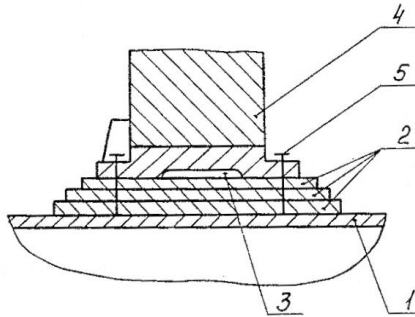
Установка укрепляющих прокладок и башмаков:
